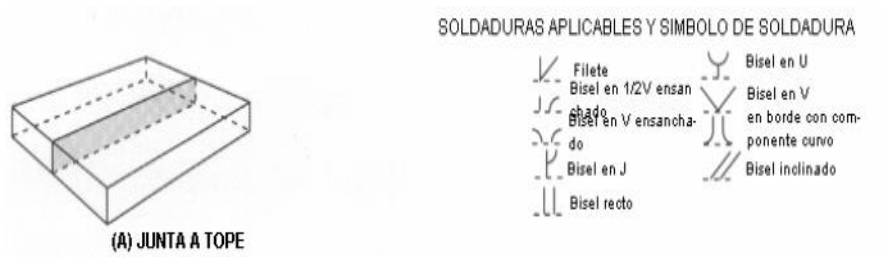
Junta Tipo Tope y la soldadura aplicable
